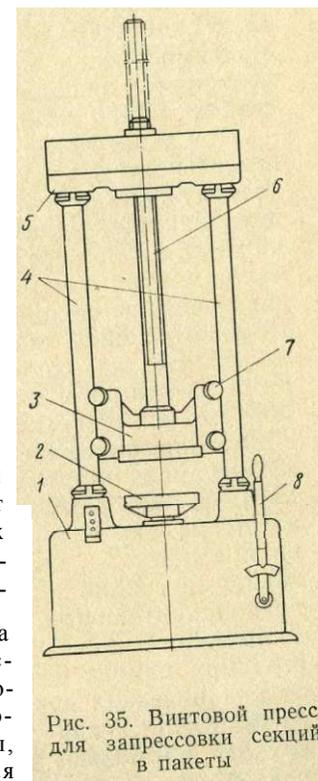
Винтовой пресс для запрессовки секций в пакеты
